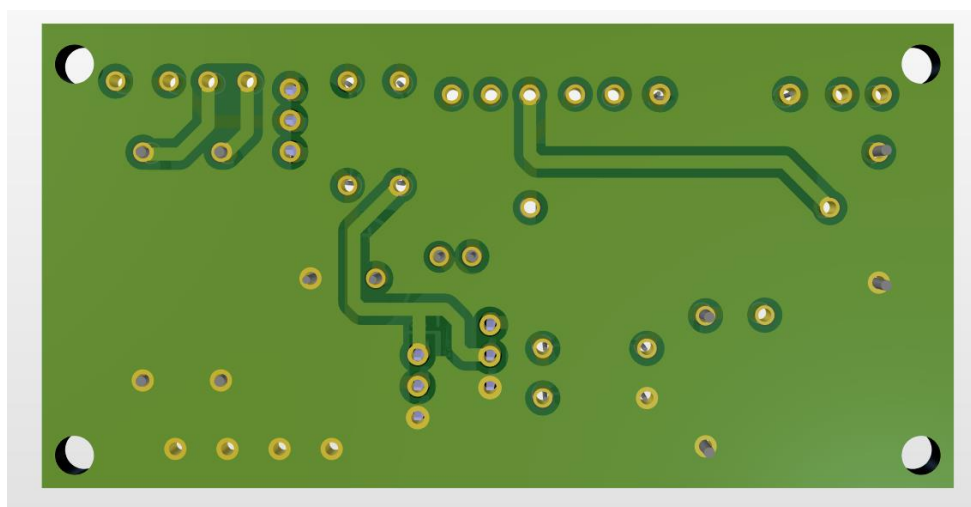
Трехмерный вид платы (нижний слой)
